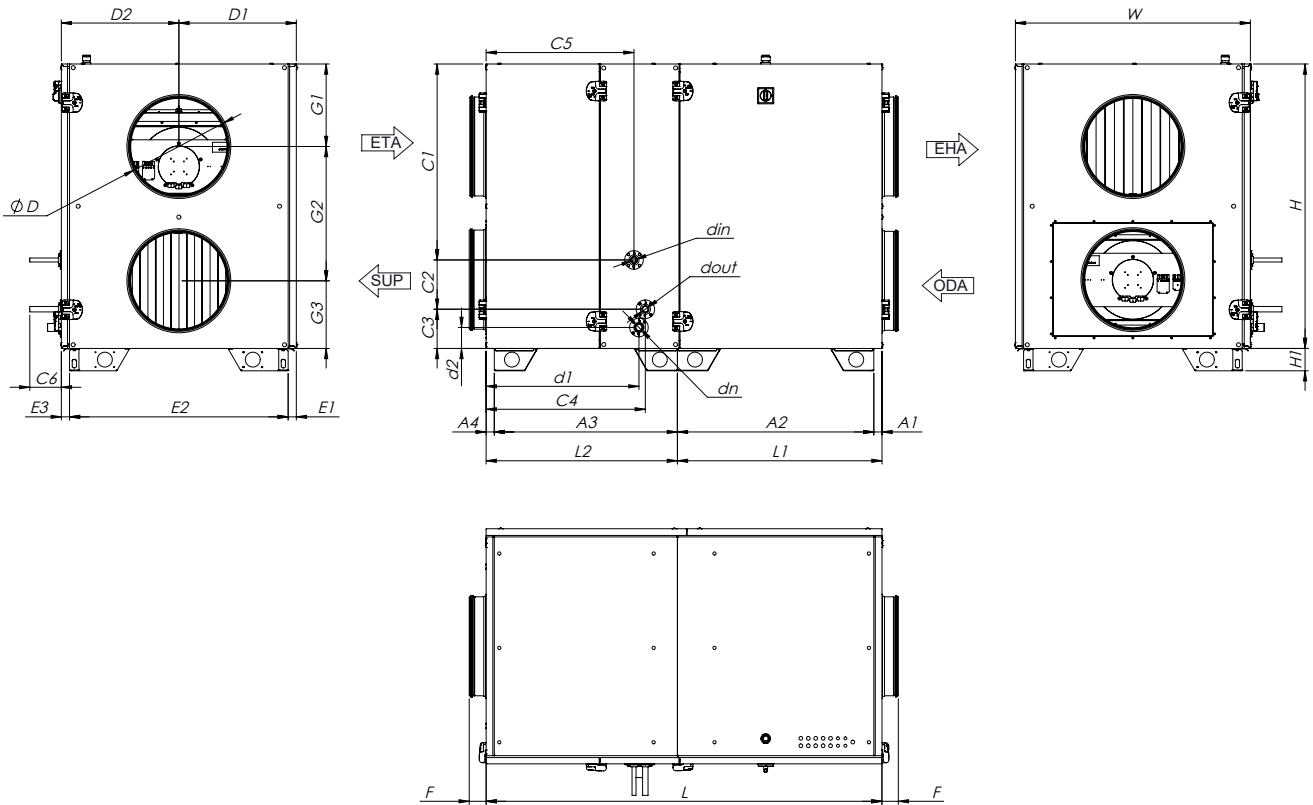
AmberAir Compact-S-R-2000-H-DX-L-C1 dimensioner
